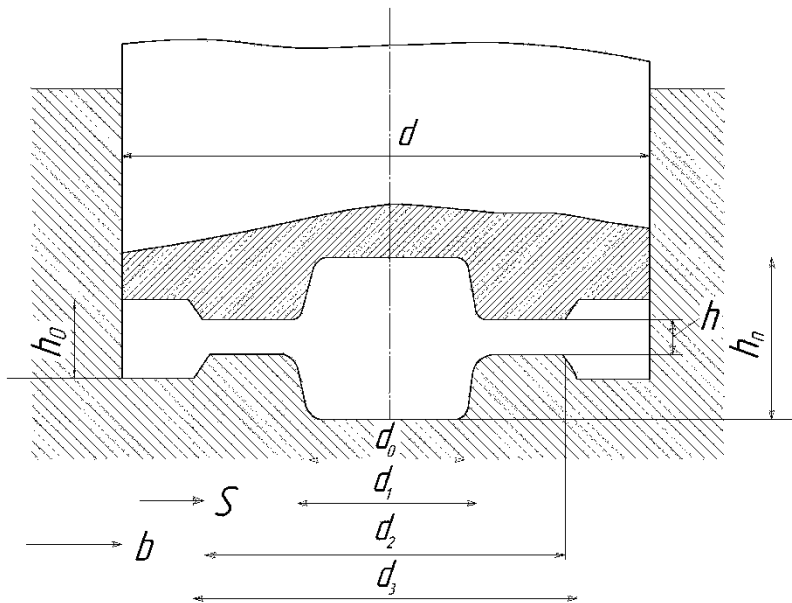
Схема завершальної фази штампування деталі типу шестерня
